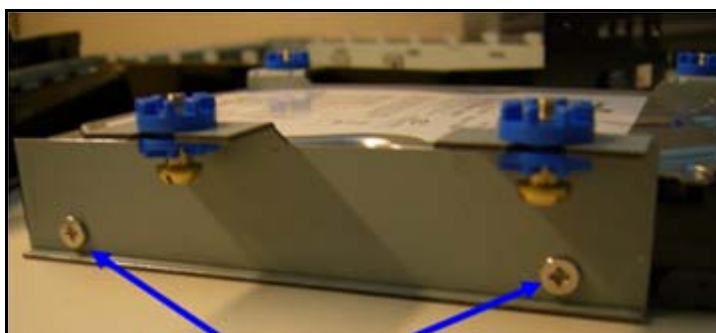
Vis des supports de montage (deux de chaque côté)
